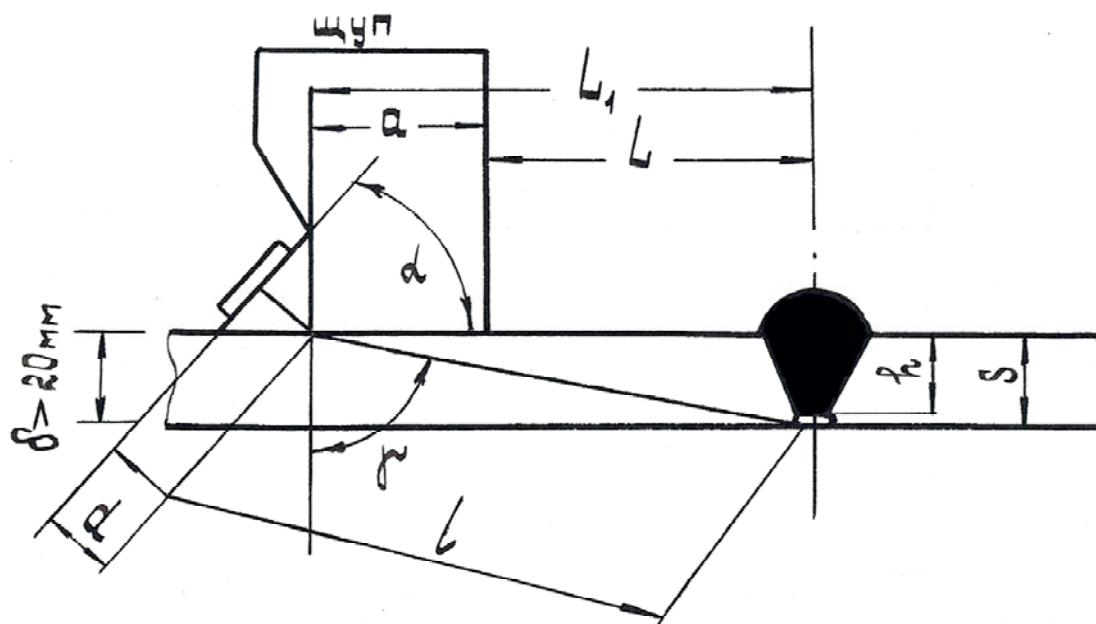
Схема прозвучивания сварного шва прямым лучом
